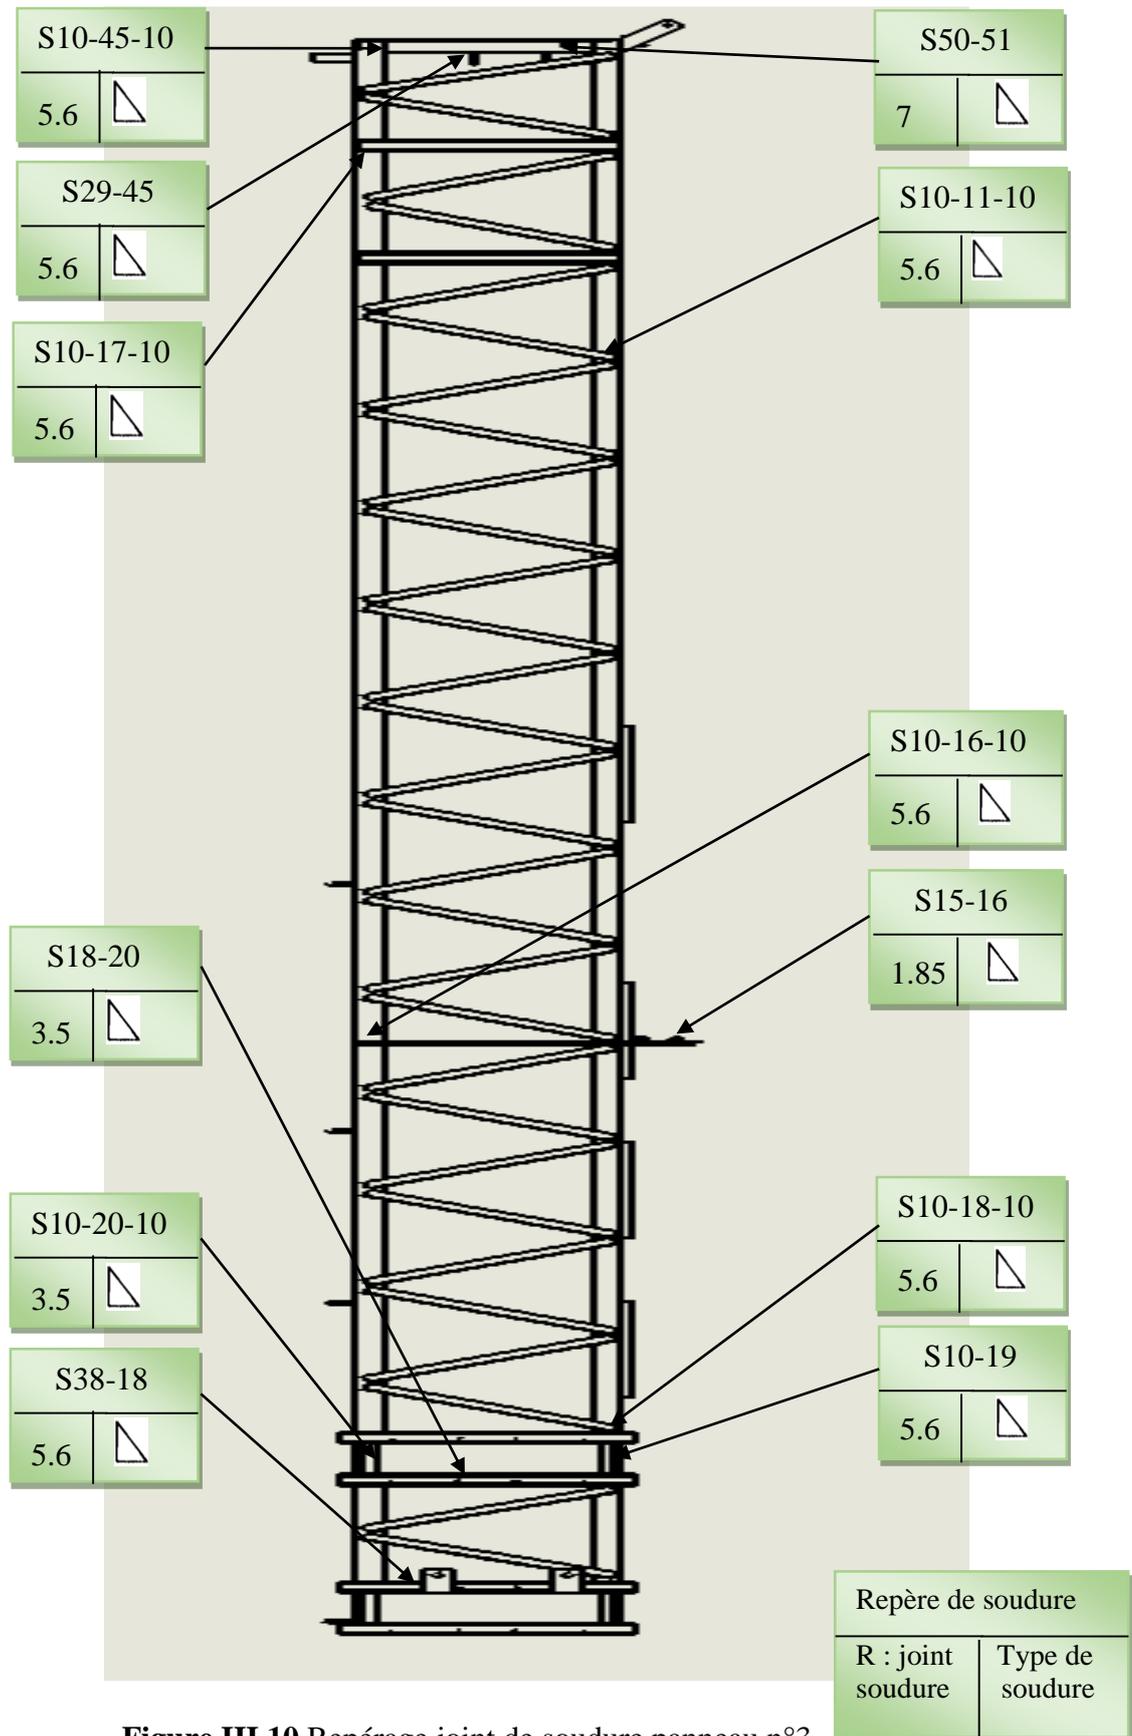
Repérage joint de soudure panneau n°3
